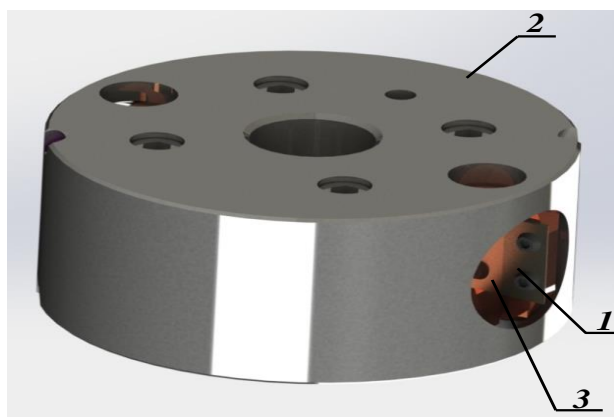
Фреза сборная с изменяемыми углами передним и наклона кромки
